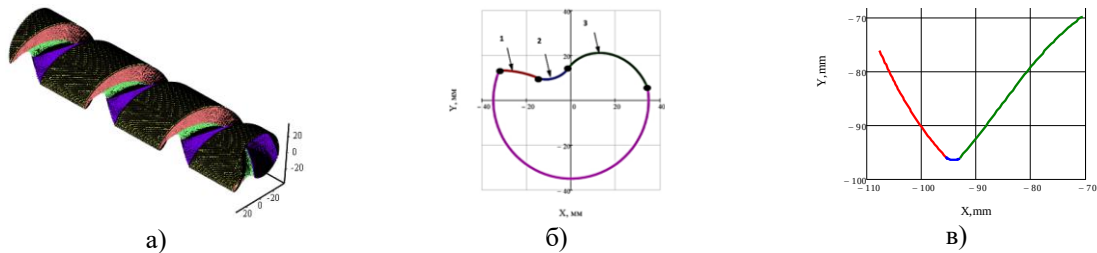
Гвинтова поверхня її торцевий перевіз і профіль інструменту призначений для її обробки: а) гвинтова поверхня; б) 1, 2, 3- твірні ділянки торцевого перерізу гвинтової поверхні, в) профіль інструмента отриманий при початкову наближенні т. 4. (рис. 1).
